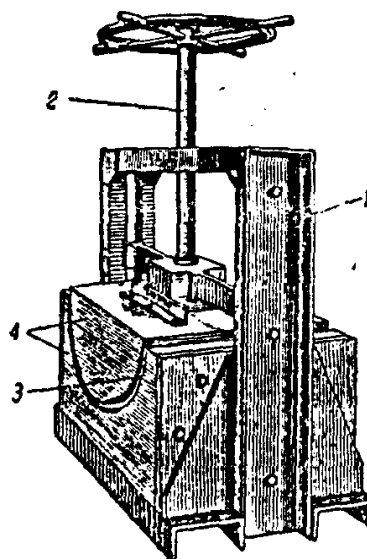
Приспособление для гнутья и склейки заготовок круглой и овальной формы.
